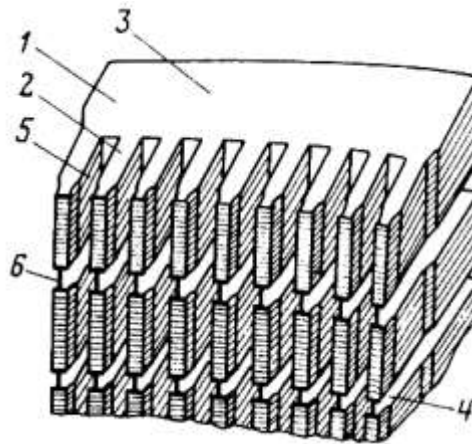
Частковий пакет сердечника статора гідрогенератора:
